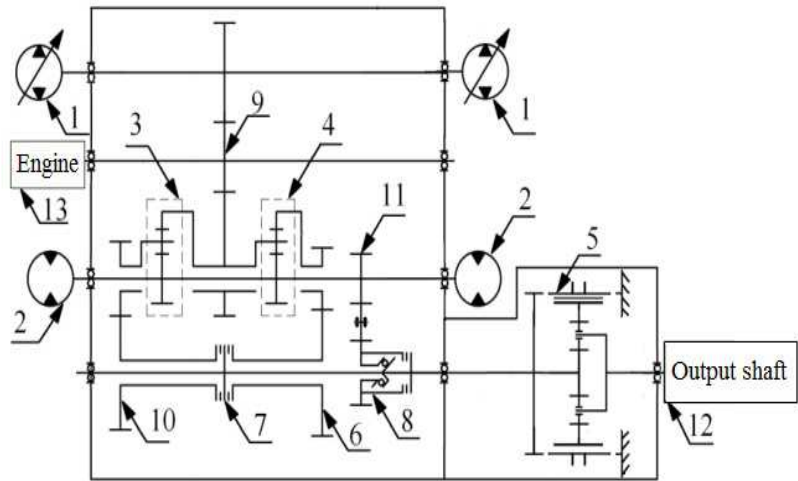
Кінематичні схеми трансмісій ГОМТ: 1 – регульований гідронасос; 2 – нерегульований гідромотор; 3, 4, 5 – планетарні механізми; 6, 9, 10, 11 – редуктори; 7 – гідропідтискні муфти; 8 – обгінна муфта; Engine – двигун внутрішнього згоряння; Output shaft – вихідний вал.
